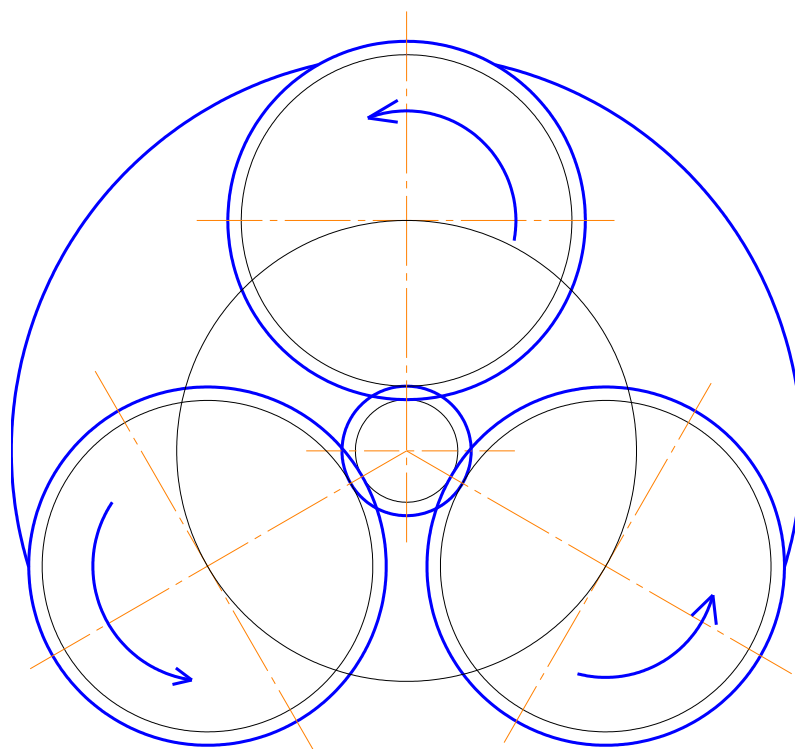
Накатывание вращающимися резьбонакатными головками
